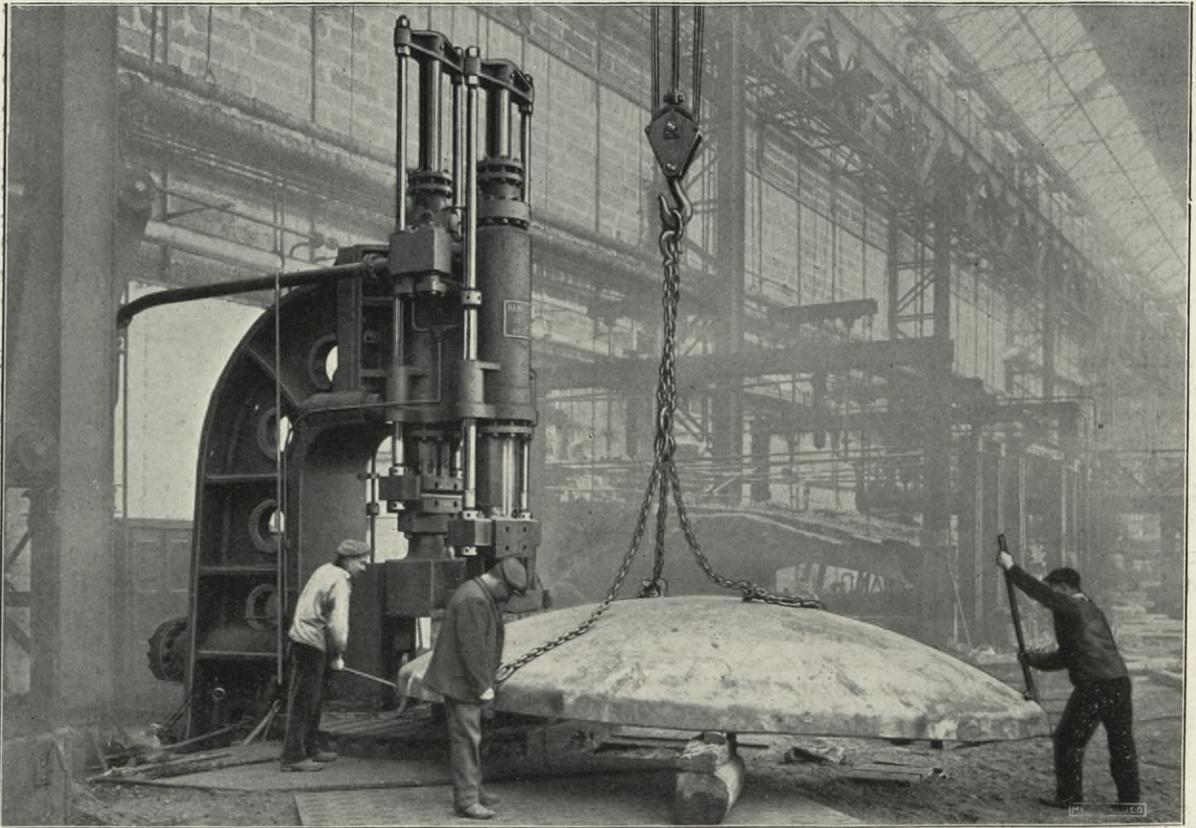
Hydraulische Flansch- und Börtelpresse. Haniel & Lueg, Düsseldorf
